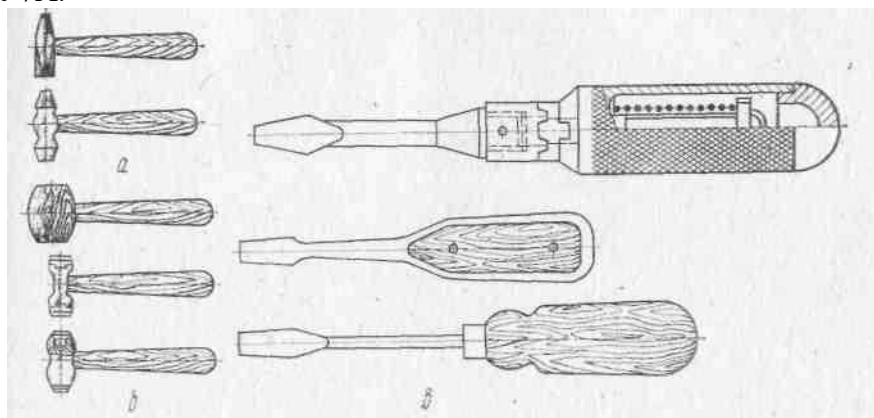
Инструменты, применяемые для разборочно-сборочных работ
